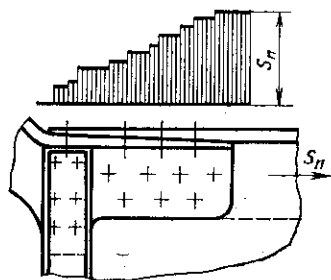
Схема крепления башмака к поясу лонжерона
